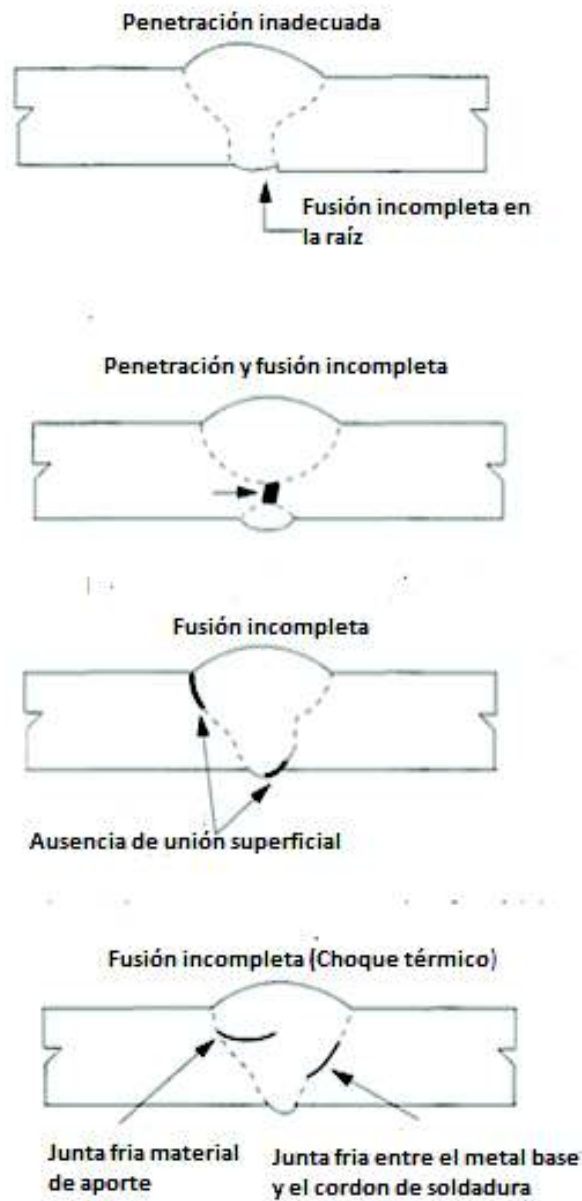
Problemas frecuentes en la soldadura.
